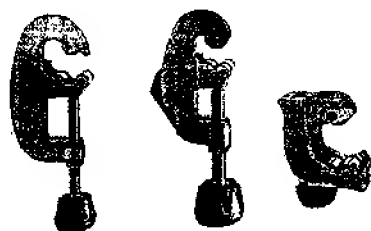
Труборезы для резки труб различного диаметра
